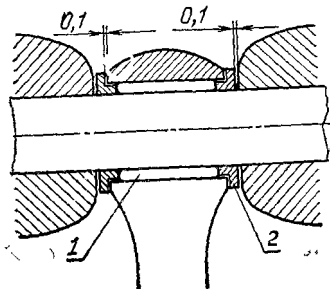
Игольчатый подшипник верхней головки шатуна:
